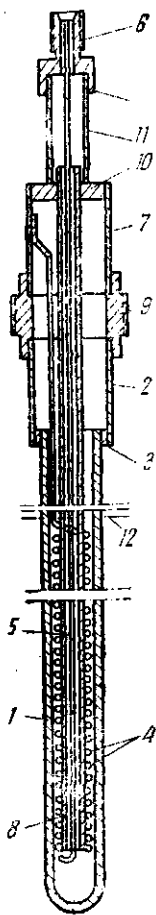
«Стратитовый» нагреватель (Шварцкоф и Левин):
